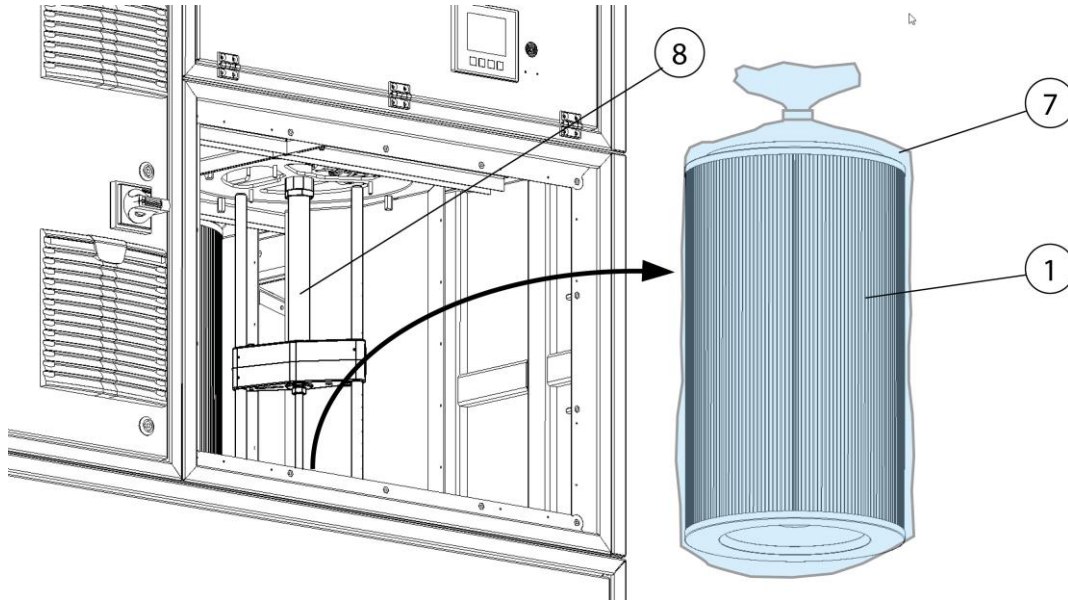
Remplacement du filtre - retrait de la cartouche filtrante
